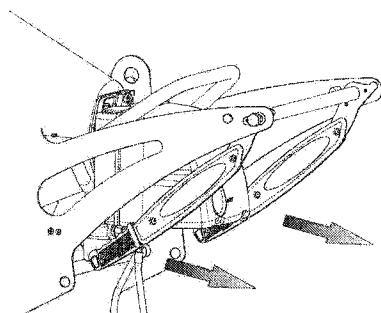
Ручки в положении готовности, нагреватель XL9.
